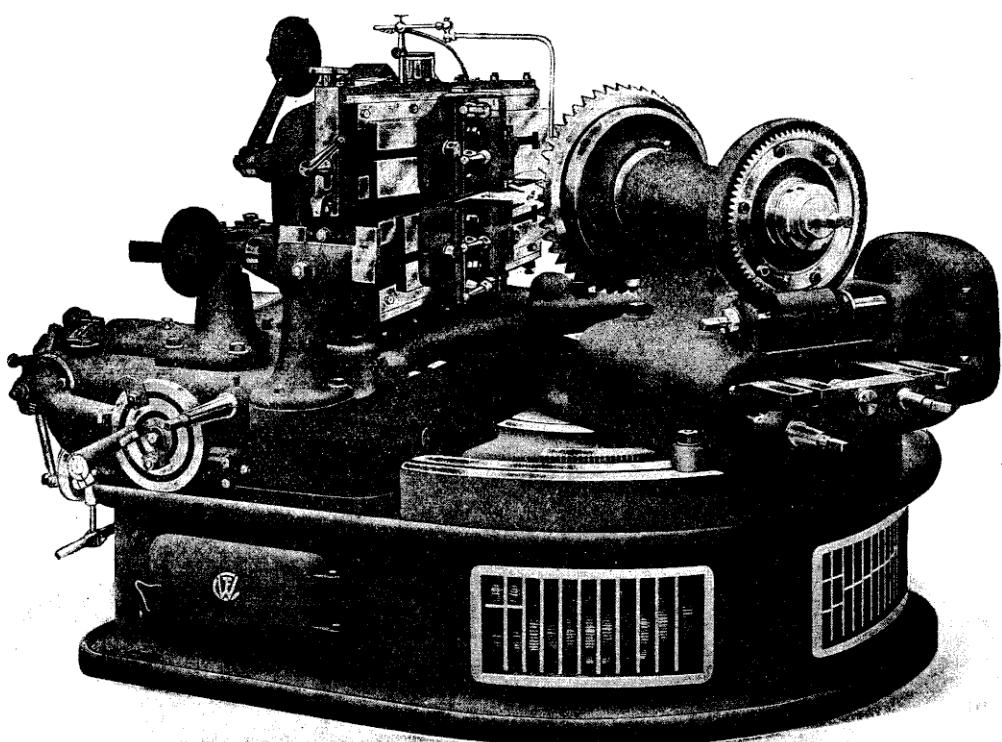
Machine automatique à tailler les engrenages coniques.
